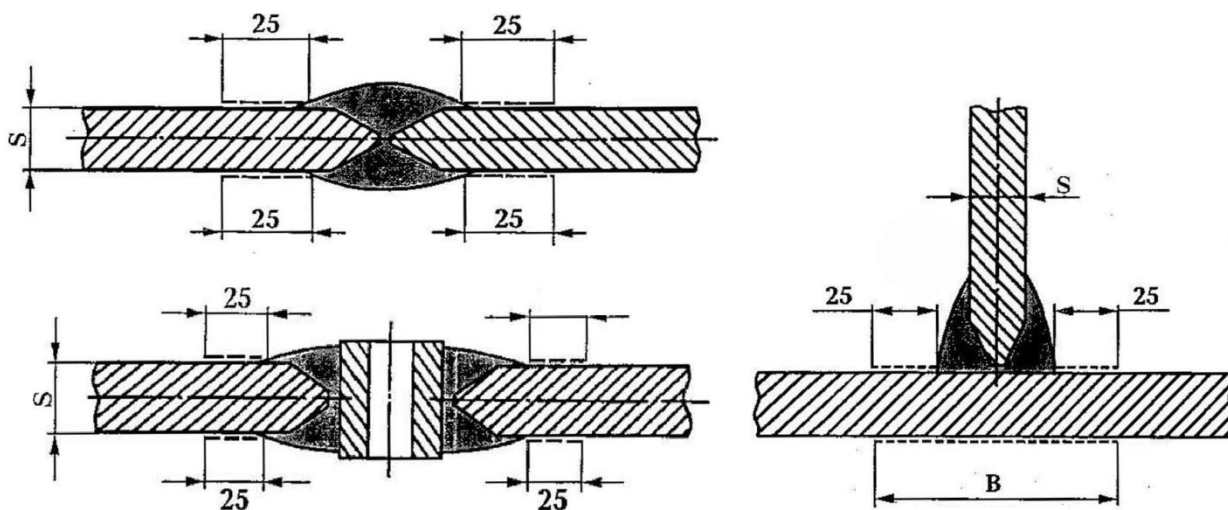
Схема обработки сварного соединения УУО с двух сторон
